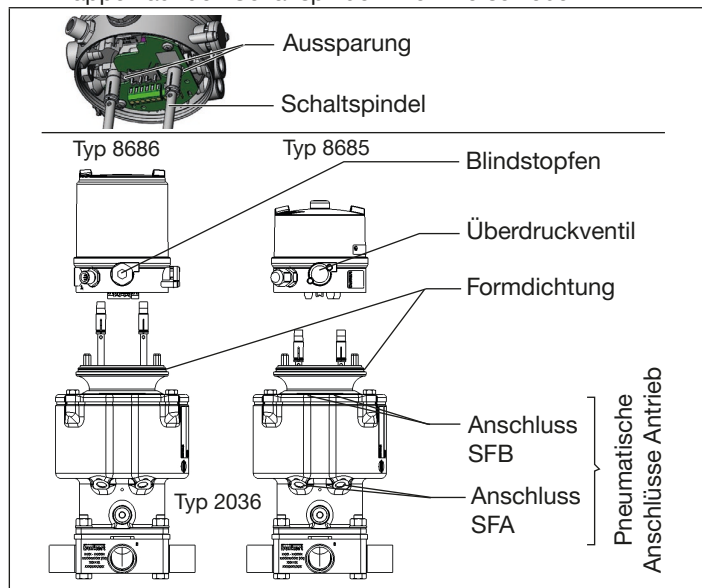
Montage Rückmeldekopf/Steuerkopf
